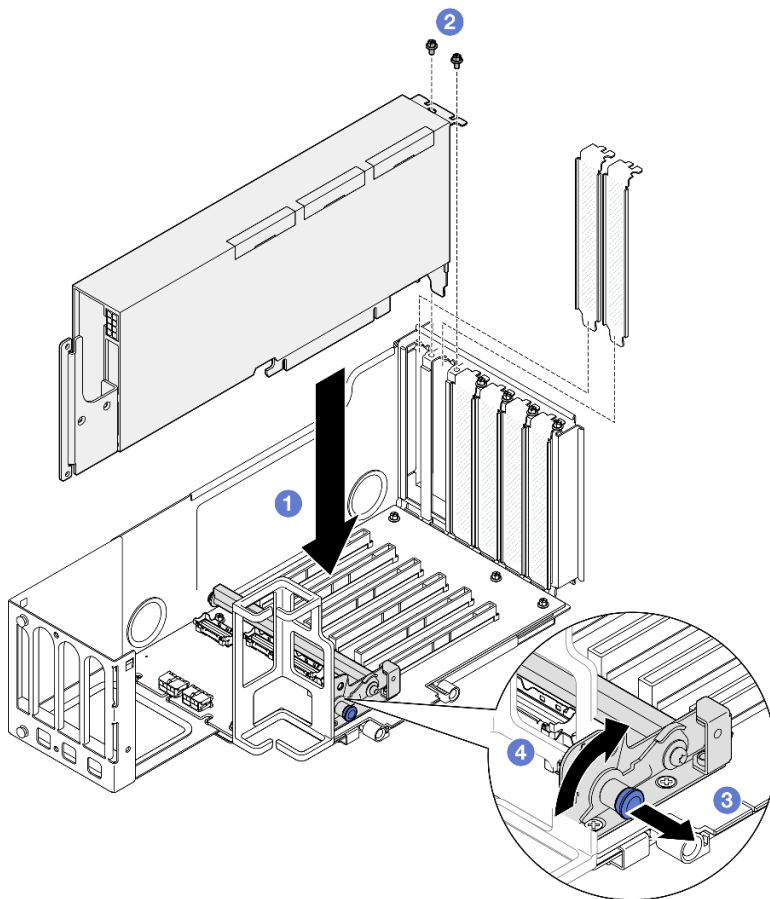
Instalando o adaptador de GPU na placa riser PCIe
